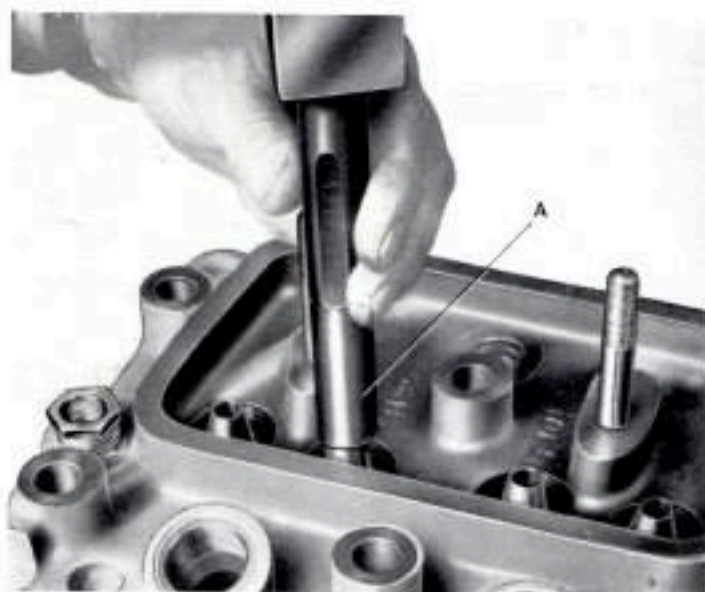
Revisionsi e controlli degli organi del motore: montaggio delle guida-valvole.
